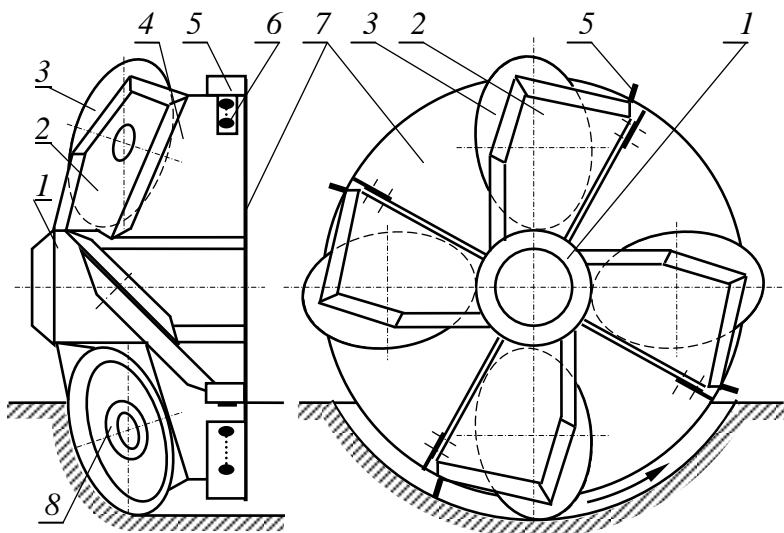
Схема фрезерного рабочего органа с дисковыми ножами.
